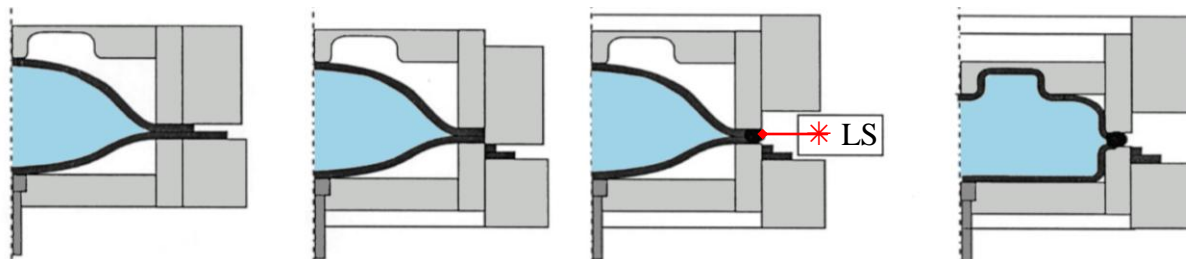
Princip tváření metodou paralelního hydroformování [12]
